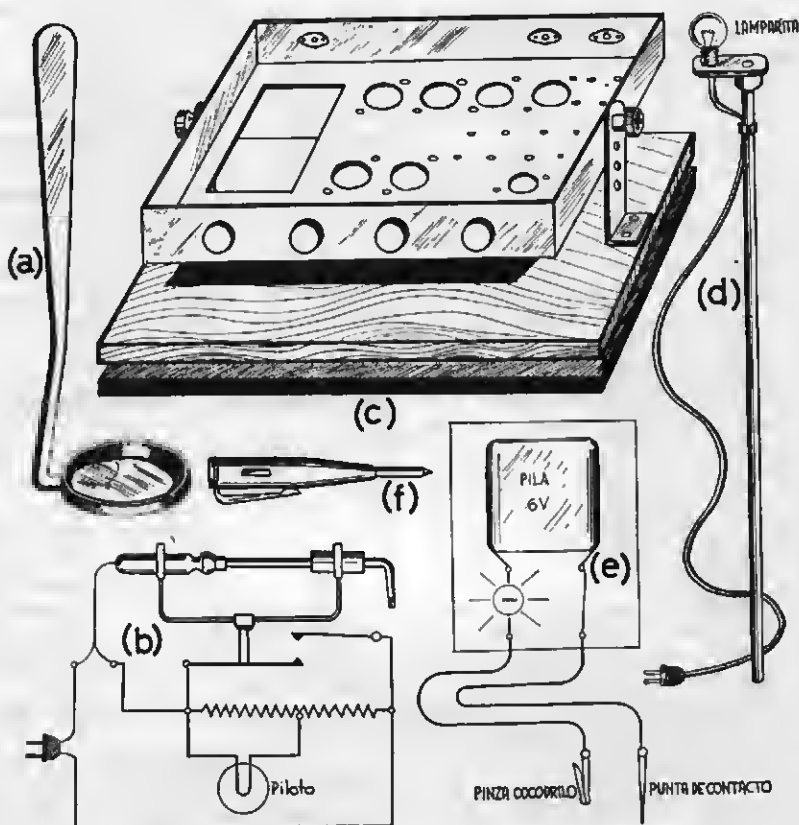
Accesorios útiles en el taller de montaje y reparación. (a), espejo explorador; (b), soporte de soldador; (c), soporte basculante para chasis; (d), lamparita exploradora; (e), probador de circuitos; (f), comprobador de tensiones.
